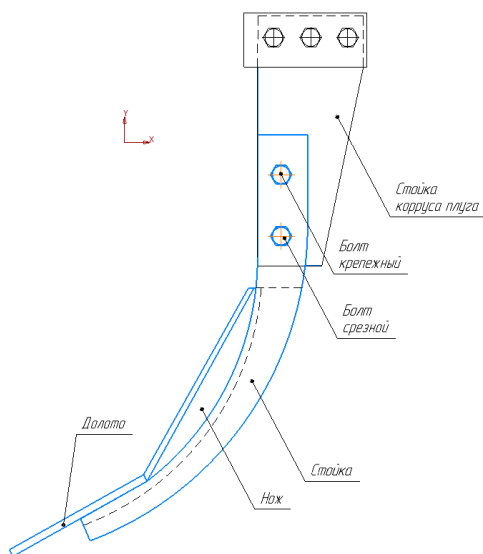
Конструкция рабочего органа глубокорыхлителя
